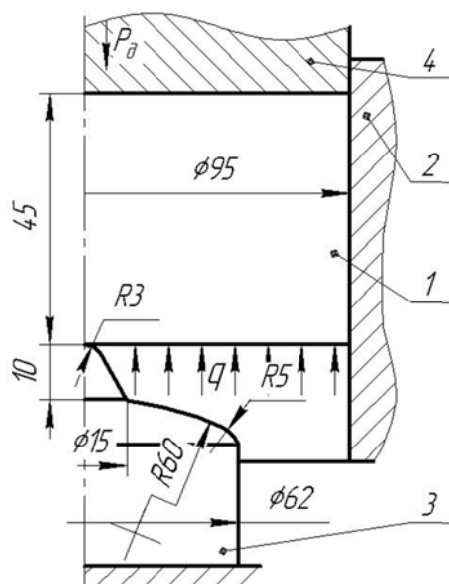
Розрахункова схема видавлювання порожнини матриці в умовах дії протитиску на вільну поверхню заготовки
